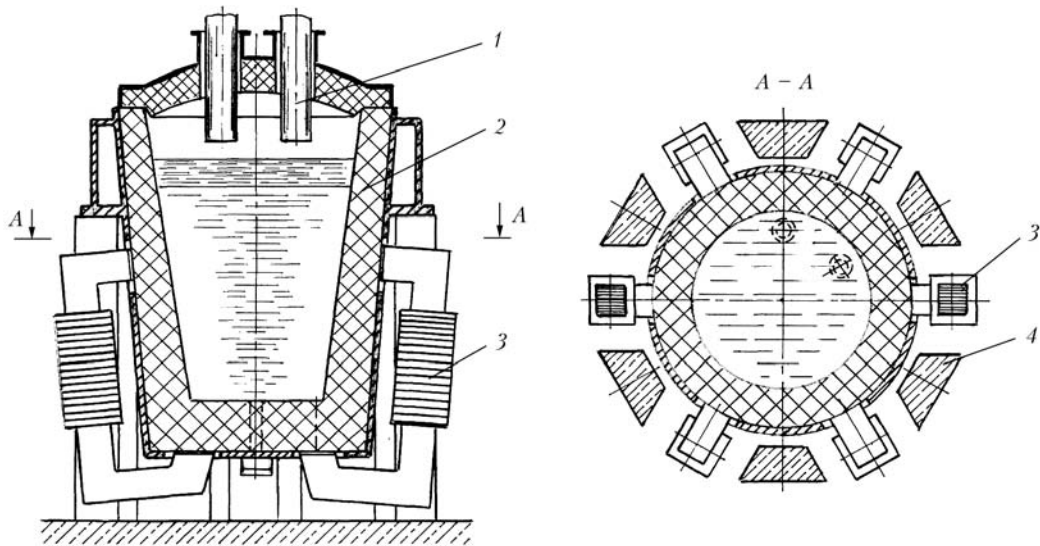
Схема гибридного индукционного ковша-печи с магнитопроводами: 1 — дуговой нагреватель; 2 — ковш; 3 — магнитопровод; 4 — опора ковша
